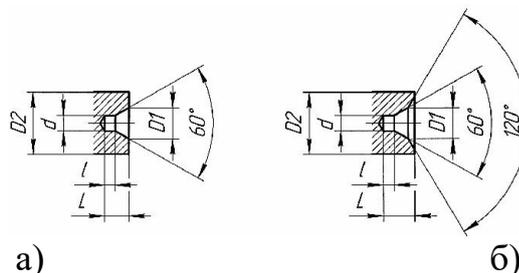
Размеры центровых отверстий: а) тип А без предохранительного конуса; б) тип Б с предохранительным конусом
